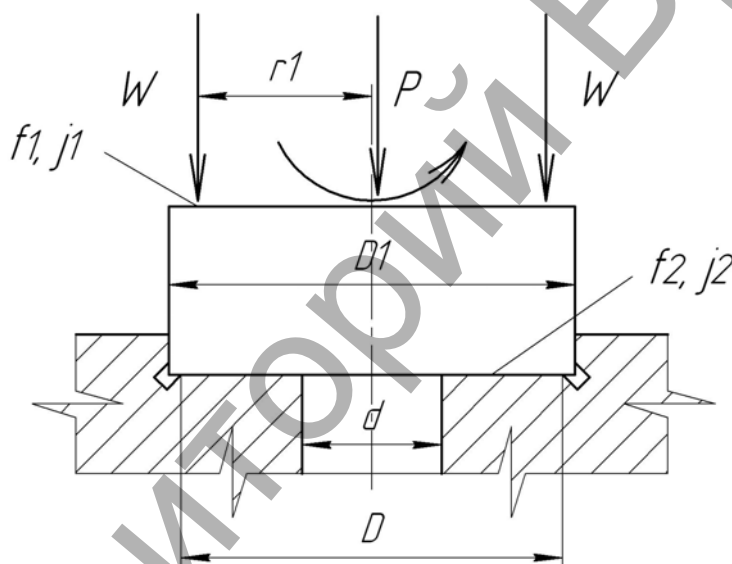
Схема сил, действующих на заготовку при ее установке по наружной поверхности
